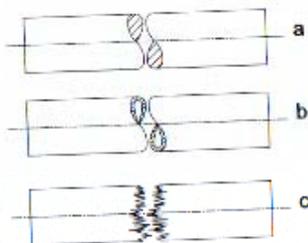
Linhas de fractura: (a) varão metálico, (b) tubo metálico e (c) madeira.
